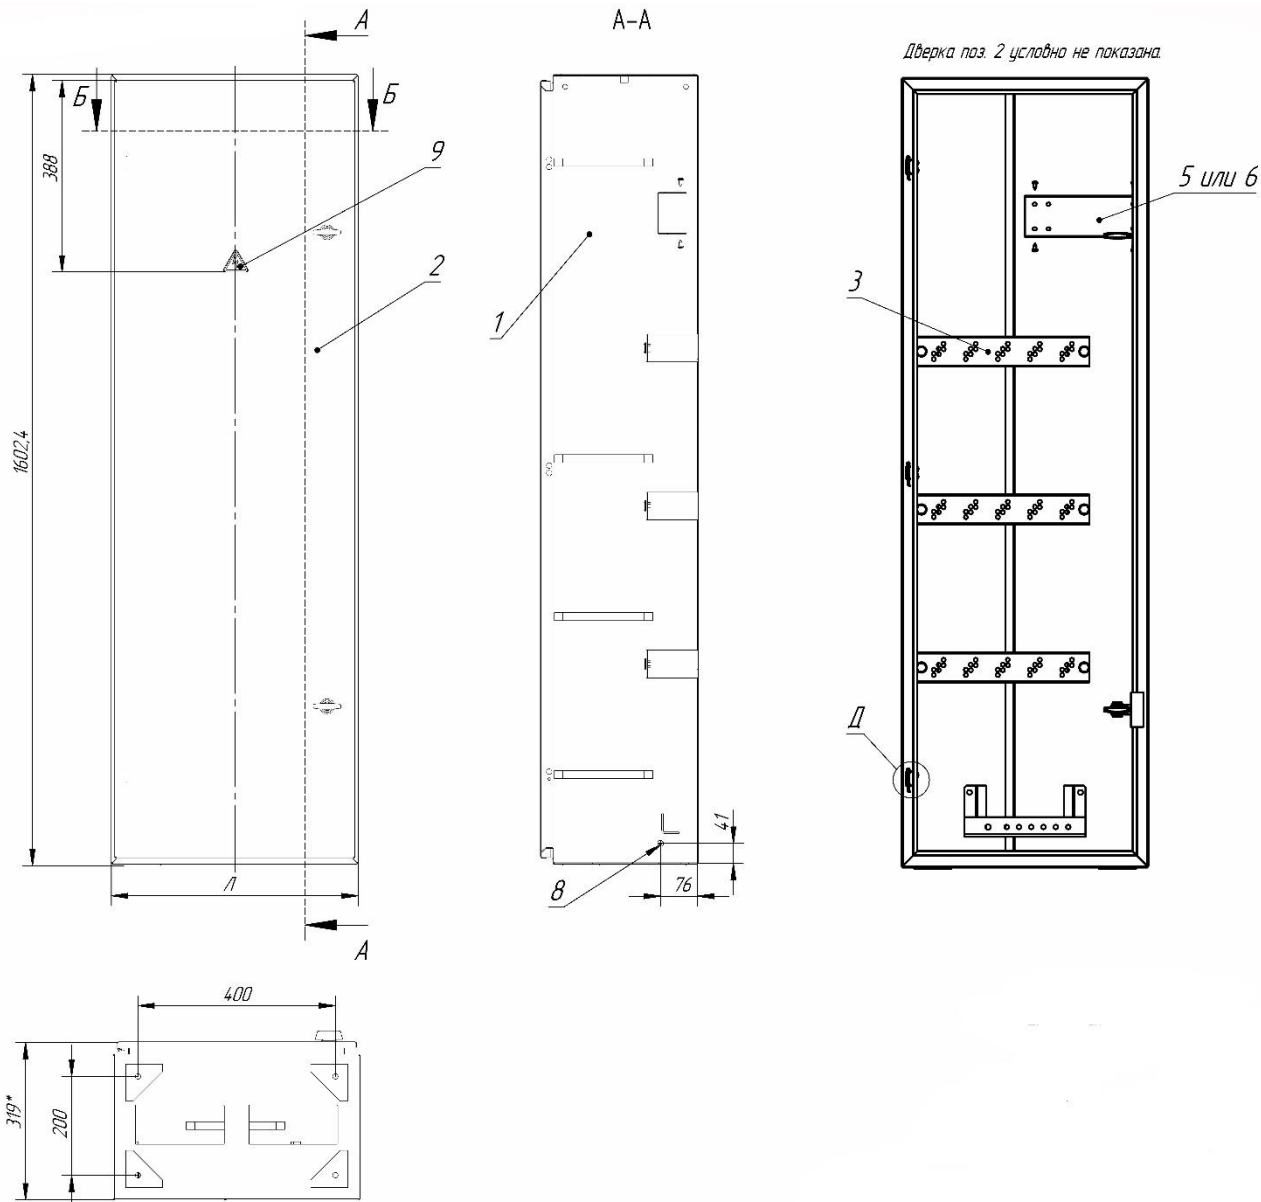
Общий вид Корпуса ШРС-1-У3-001.
